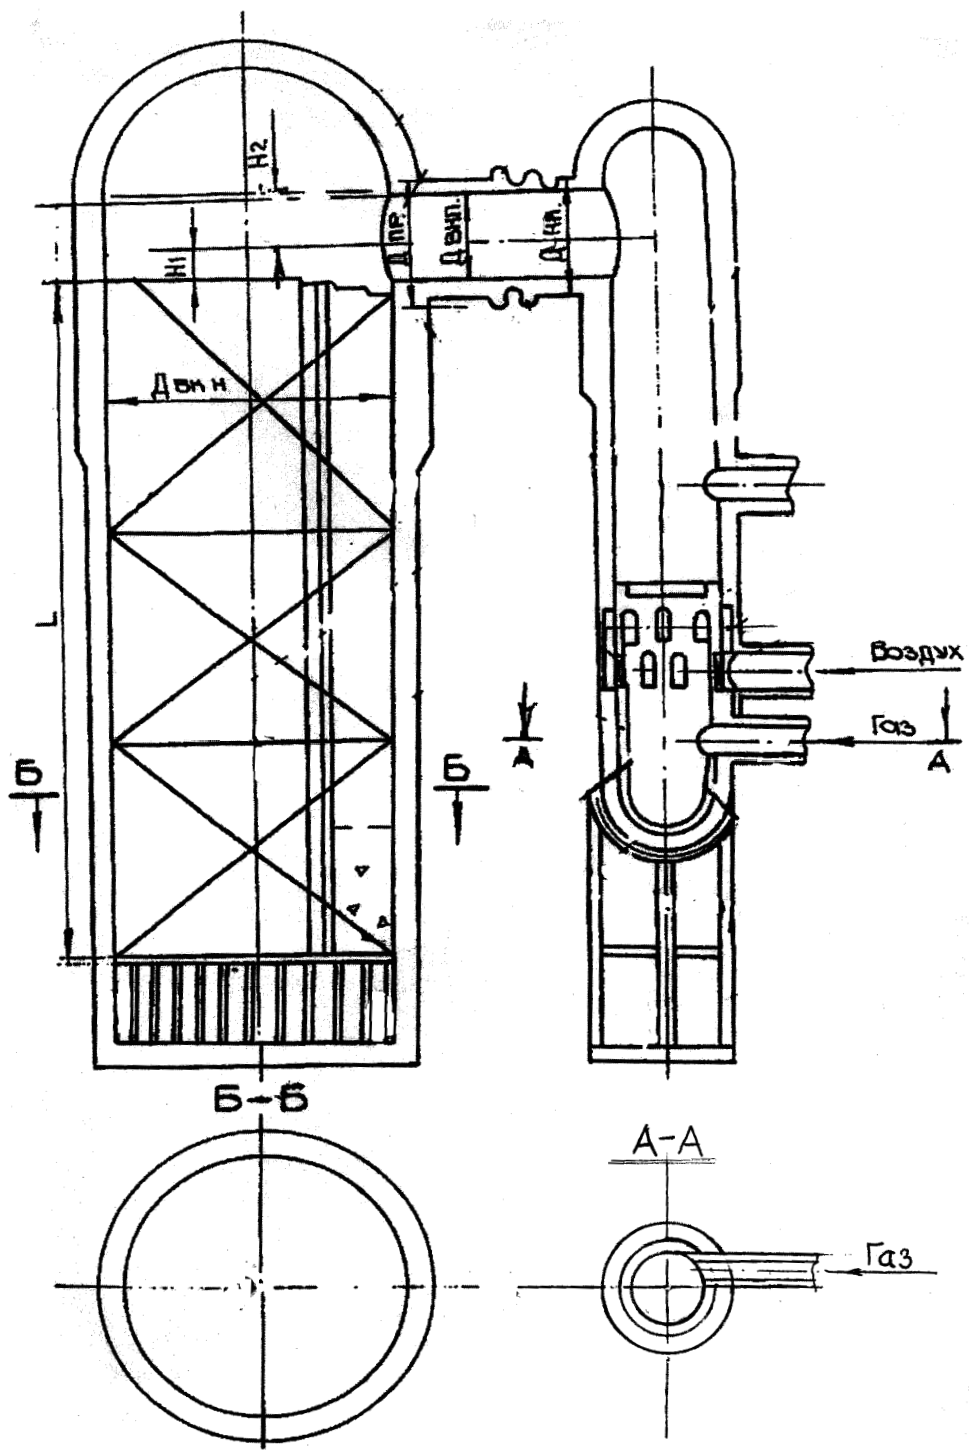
Реконструкция воздухонагревателя с внутренней камерой горения на воздухонагреватель для отопления его керамической струйно-факельной горелкой, располагаемой вертикально в нижней части вынесенной камеры горения
